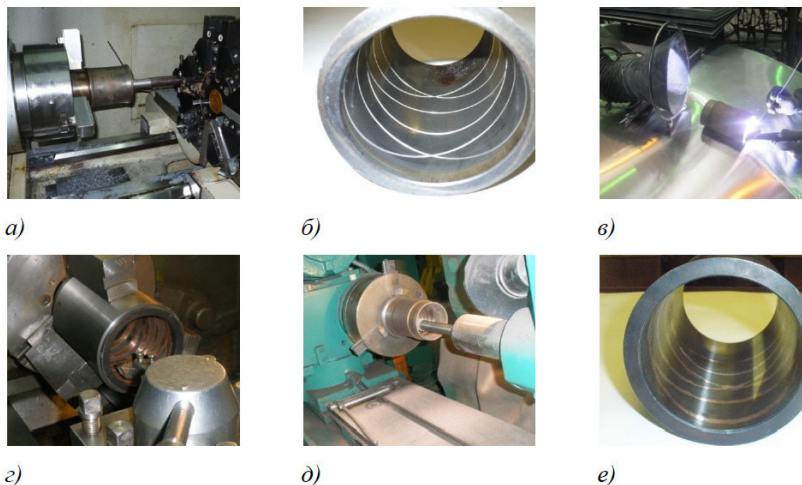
Технологический процесс изготовления металлизированной медью гильзы цилиндров: а)нарезка кольцевых канавок; б) гильза с нарезанными кольцевыми канавками; в) наплавка канавок медью; г) зачистка внутренней поверхности; д) шлифование внутренней поверхности; е) металлизированная гильза цилиндров
